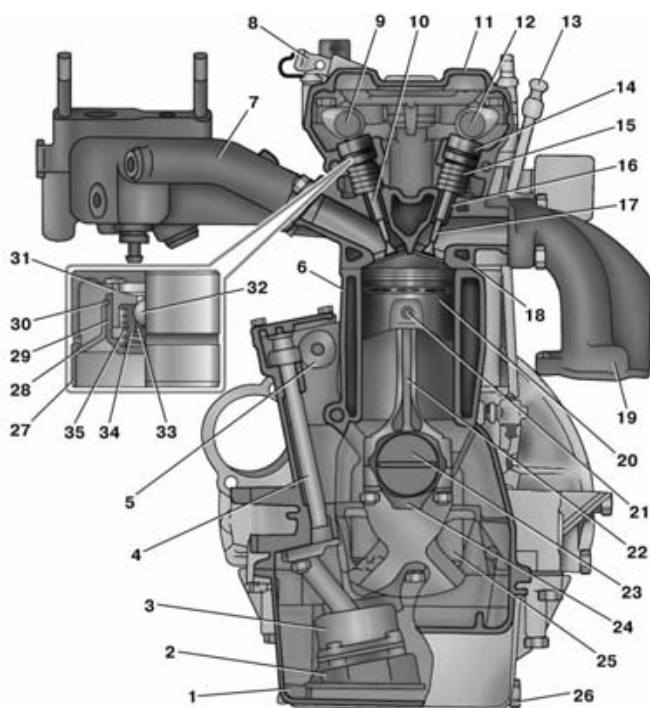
Поперечный разрез двигателей мод. ЗМЗ-4061 и ЗМЗ-4063: 1 – масляный картер; 2 – приемник масляного насоса; 3 – масляный насос; 4 – привод масляного насоса; 5 – шестерня промежуточного вала; 6 – блок цилиндров; 7 – впускная труба; 8 – патрубки вентиляции; 9 – распределительный вал впускных клапанов; 10 – впускной клапан; 11 – крышка клапанов; 12 – распределительный вал выпускных клапанов; 13 – указатель (щуп) уровня масла; 14 – гидротолкатель клапана; 15 – наружная пружина клапана; 16 – направляющая втулка клапана; 17 – выпускной клапан; 18 – головка блока цилиндров; 19 – выпускной коллектор; 20 – поршень; 21 – поршневой палец; 22 – шатун; 23 – коленчатый вал; 24 – крышка шатуна; 25 – крышка коренного подшипника; 26 – сливная пробка; 27 – корпус толкателя; 28 – направляющая втулка; 29 – корпус компенсатора; 30 – стопорное кольцо; 31 – поршень компенсатора; 32 – шариковый клапан; 33 – пружина шарикового клапана; 34 – корпус шарикового клапана; 35 – разжимная пружина.
